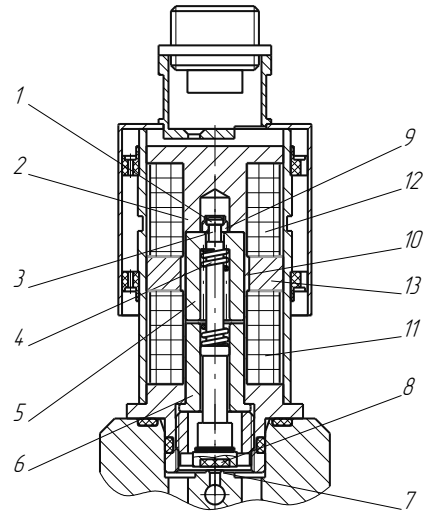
Конструктивна схема клапана з двопозиційним електромагнітним приводом: 1 – головка штока; 2 – корпус електромагніта; 3 – шийка штока; 4 – буферна пружина; 5 – повзун (якір); 6 – нижній стоп; 7 – сідло; 8 – золотник; 9 – стопорна шайба; 10 – трубка розподільна; 11 – обмотка закриття; 12 – обмотка відкриття; 13 – постійний магніт
